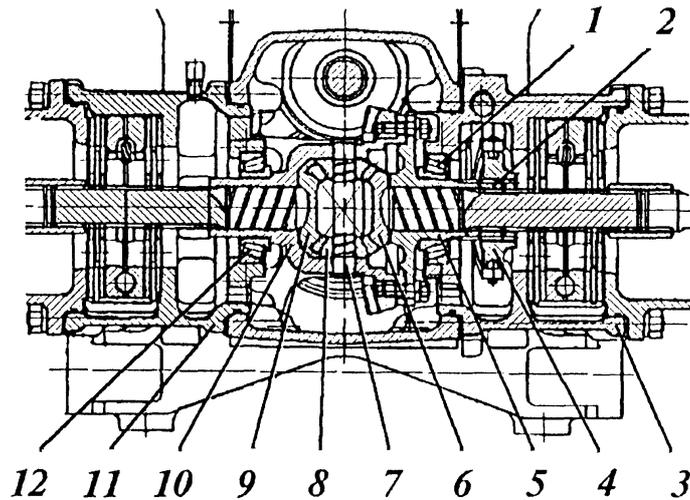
Дифференциал: 1, 12- подшипники; 2 - втулка; 3, 11-корпусы тормоза; 4 - муфта; 5 - крышка дифференциала; 6, 9 - полуосевые шестерни; 7 - ось сателлитов; 8 - сателлит; 10-корпус дифференциала
